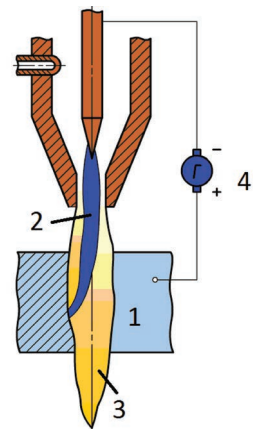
Формирование кромки реза: 1 — заготовка, 2 — электрическая дуга, 3 — факел плазмы, 4 — генератор тока.
